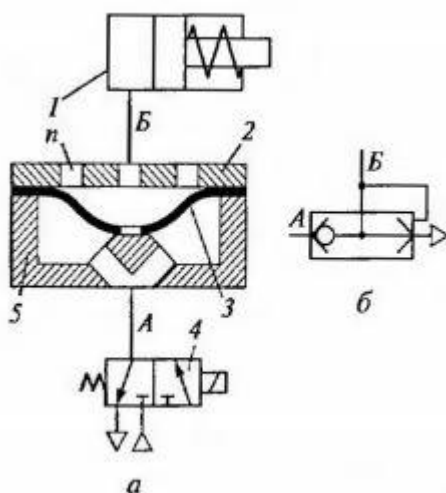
Клапан быстрого выхлопа: а - схема включения в пневмосеть; б - условное обозначение; 1 - пневмоцилиндр; 2 - крышка; 3 - мембрана; 4 - распределитель; 5 – корпус.
